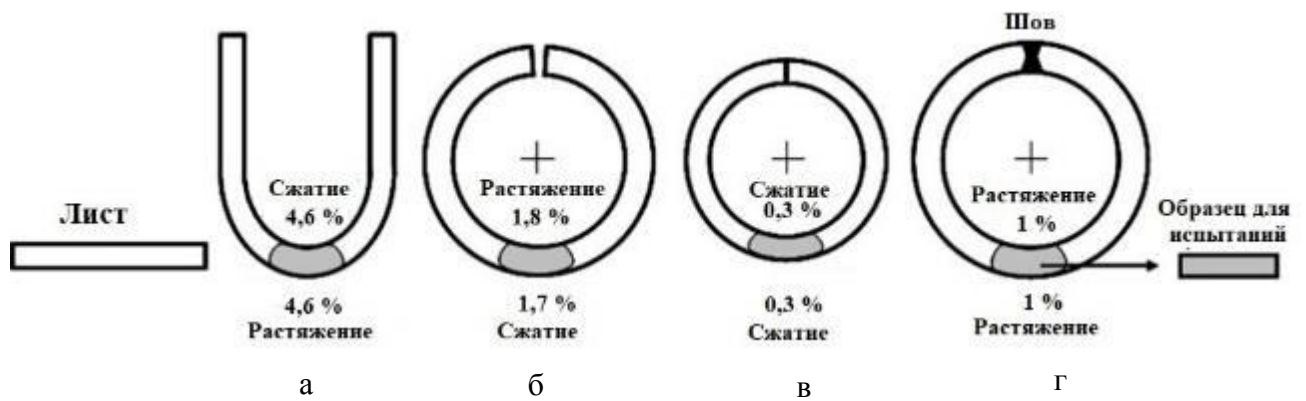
Пример УОЕ формовки трубной заготовки при производстве прямошовной сварной трубы размером 914×25 мм [66]:
